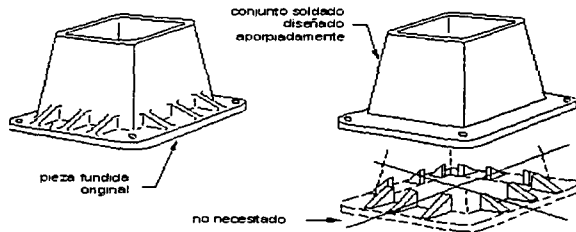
Conjunto soldado reemplazado por una pieza fundida.
